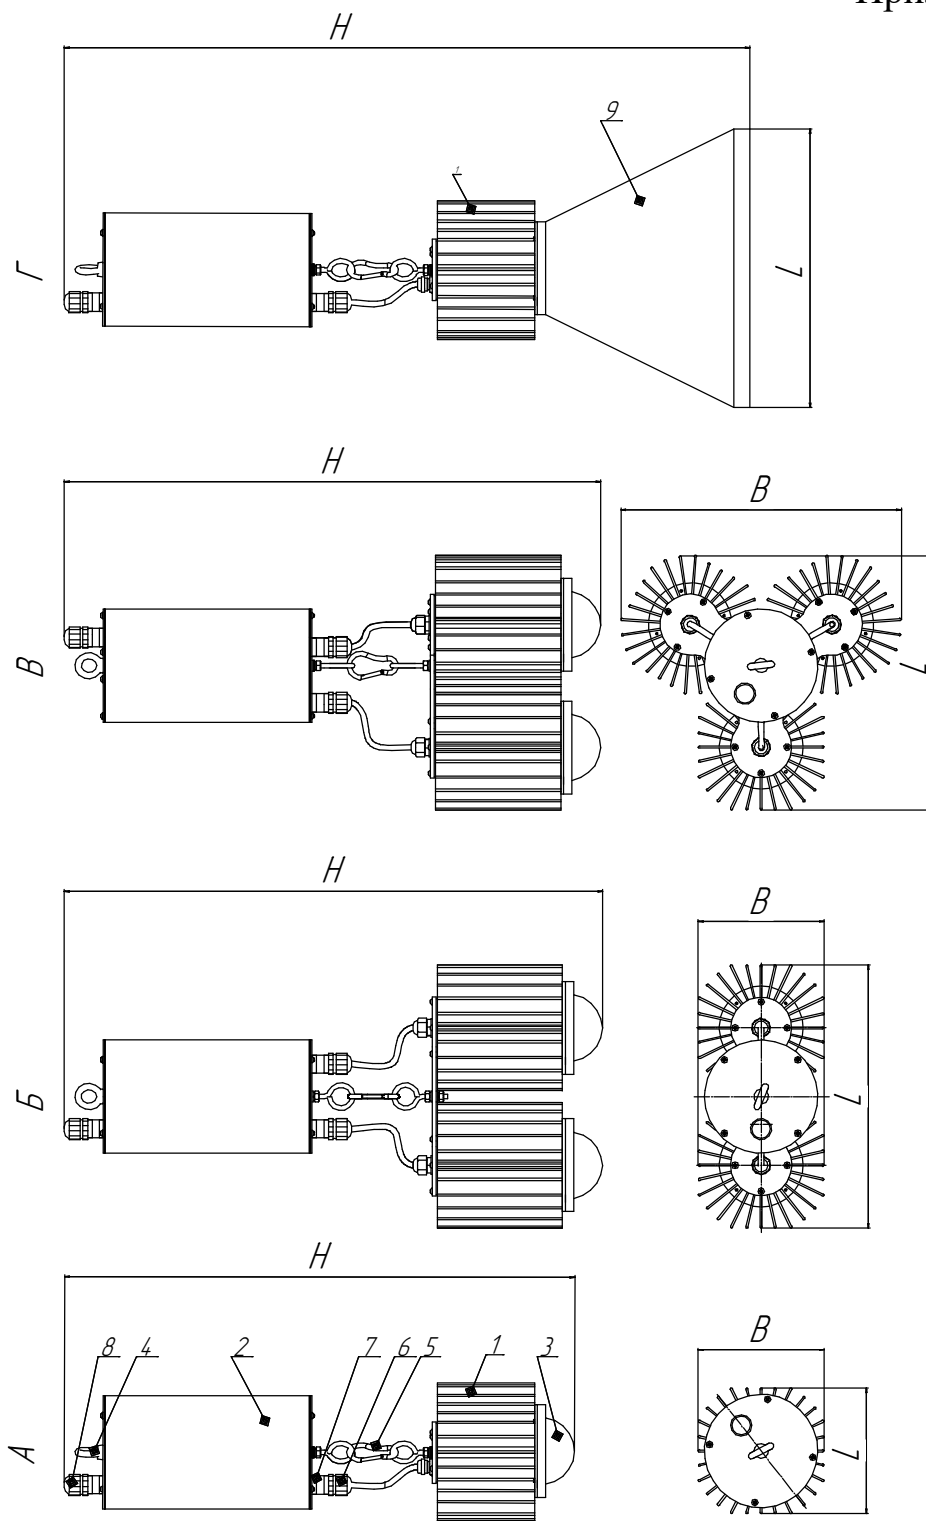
Внешний вид и габаритные размеры светильников.
